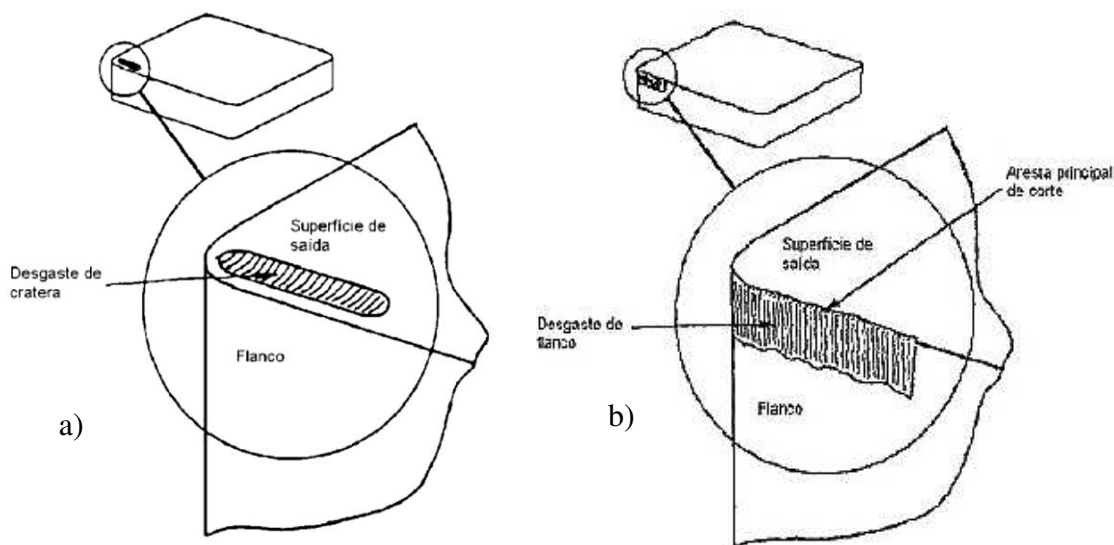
Representação esquemática dos desgastes de cratera (a) e de flanco (b).
